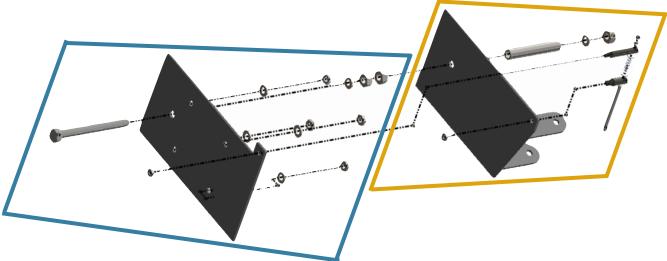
Vista isométrica del explosionado para el montaje del sistema de agarre de la amoladora. Fuente: elaboración propia.
